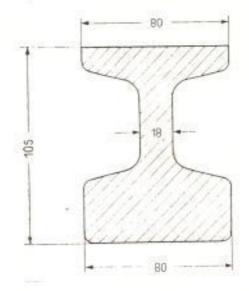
PERFIL Y DIMENSIONES (MM) DEL CARRIL DE CONTACTO.
